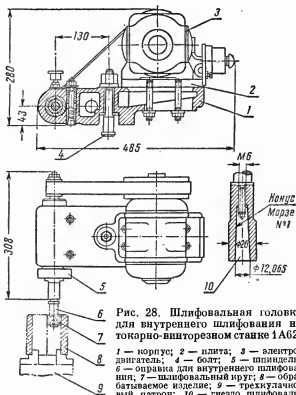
Шлифовальная головка для внутреннего шлифования на токарно-винторезном станке 1А62:
